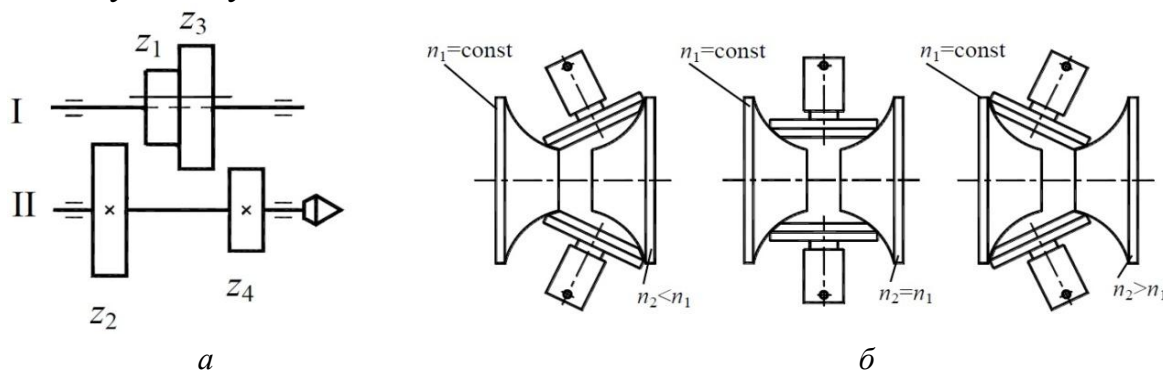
Типовые механизмы: *а* — коробка скоростей с подвижным блоком зубчатых колёс; *б* — торовый вариатор
